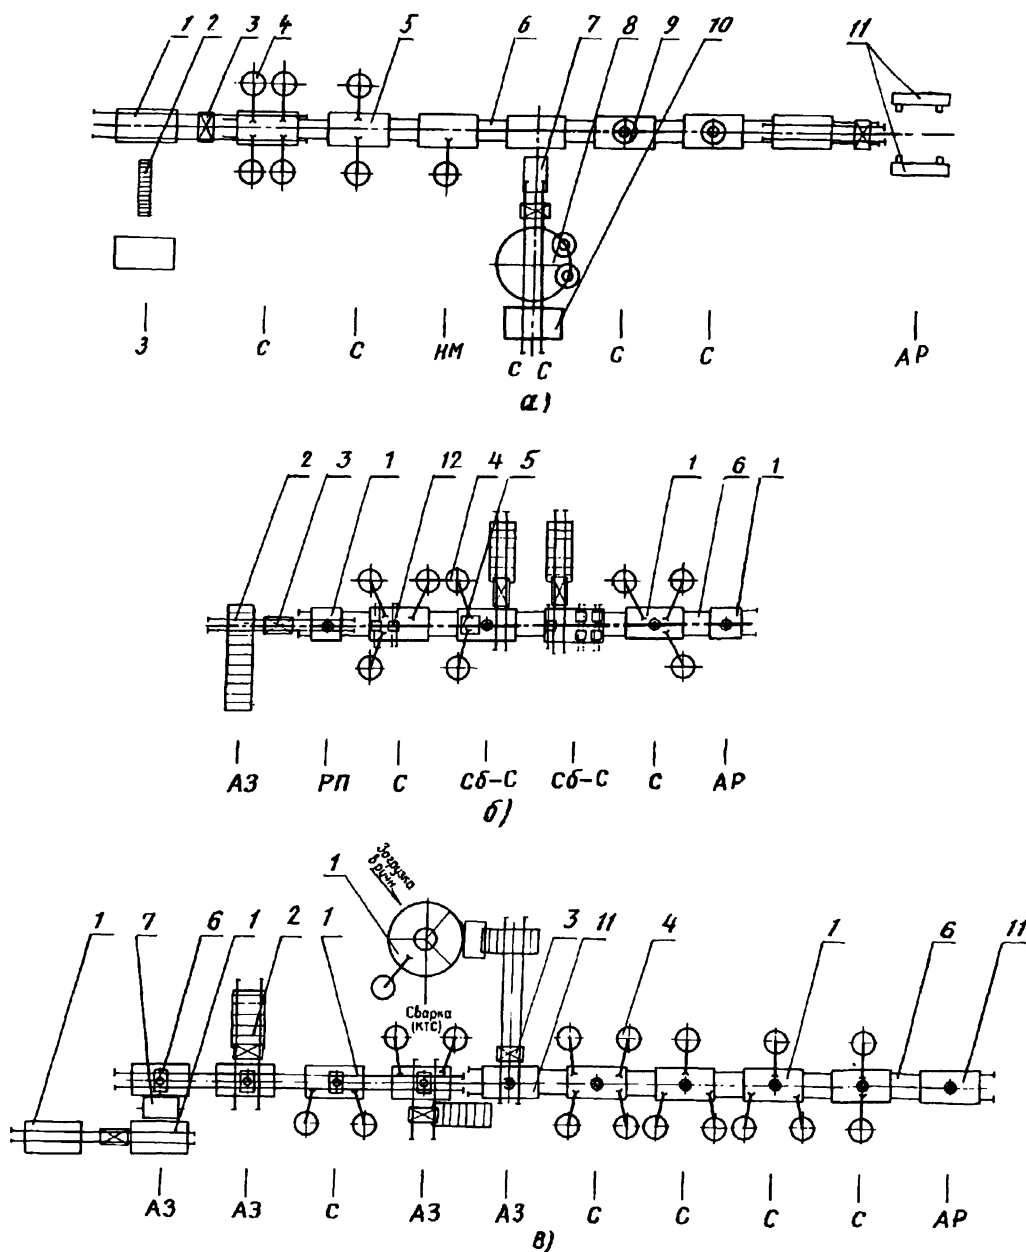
Линия сборки-сварки автомобиля:
